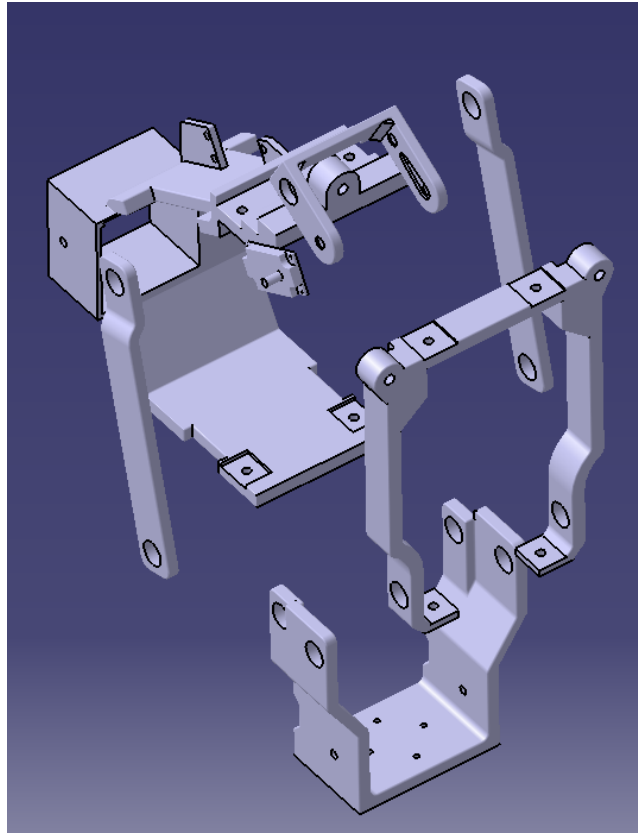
Despiece del conjunto de piezas del subensamblaje superior.
